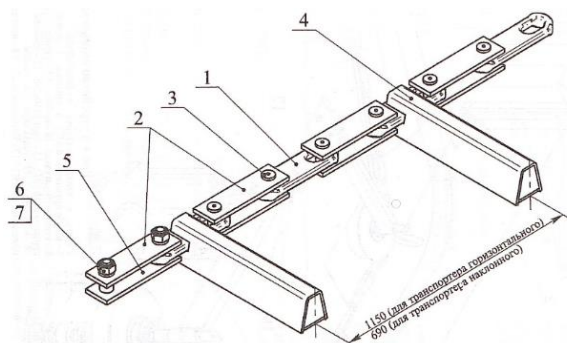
Рабочий орган транспортера ТСН-3.0Б: 1 – внутреннее звено; 2 – планка; 3 – палец; 4 – скребок; 5 – звено соединительное; 6 – гайка М16; 7 – шайба пружинная 16.65Г
